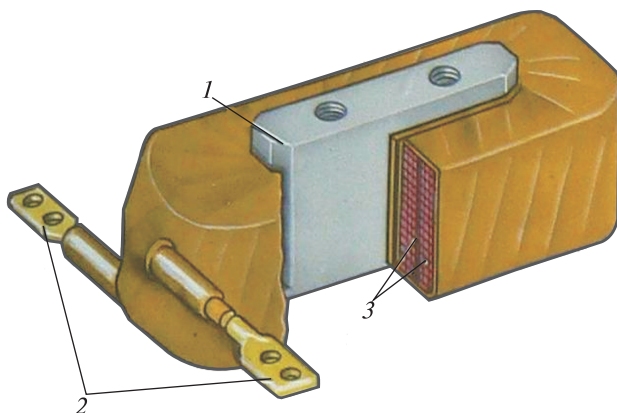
Дополнительный полюс электродвигателя НБ-431:
